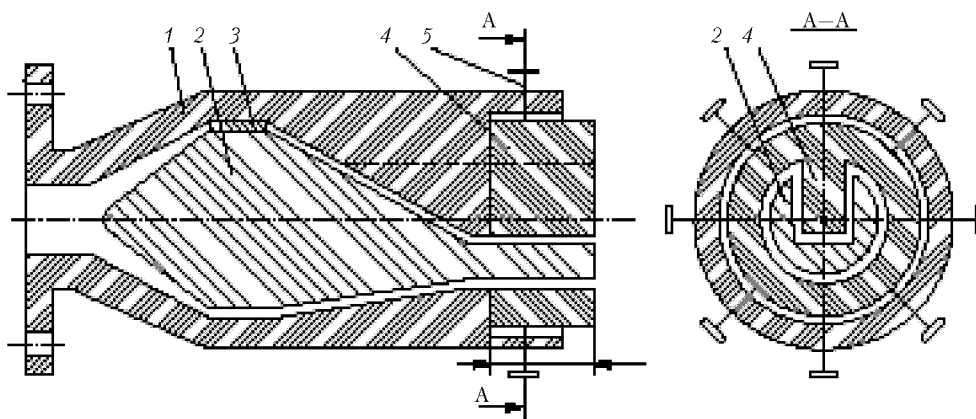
Схема формирующей головки для изготовления сложного полого профиля: 1 — корпус; 2 — дорн; 3 — дорнодержатель; 4 — мундштук; 5 — регулировочные винты
